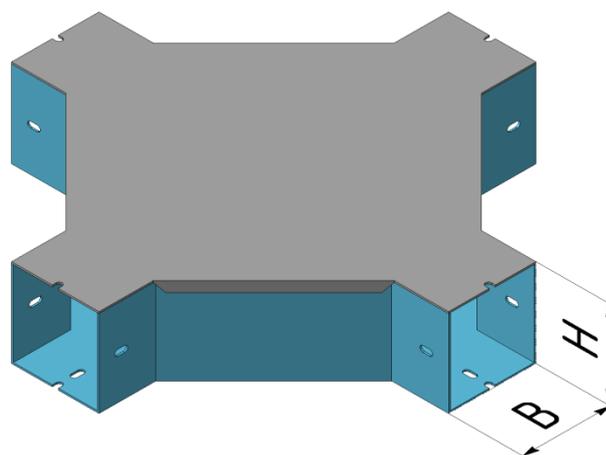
Короб угловой на четыре направления типа КХ. Общий вид
